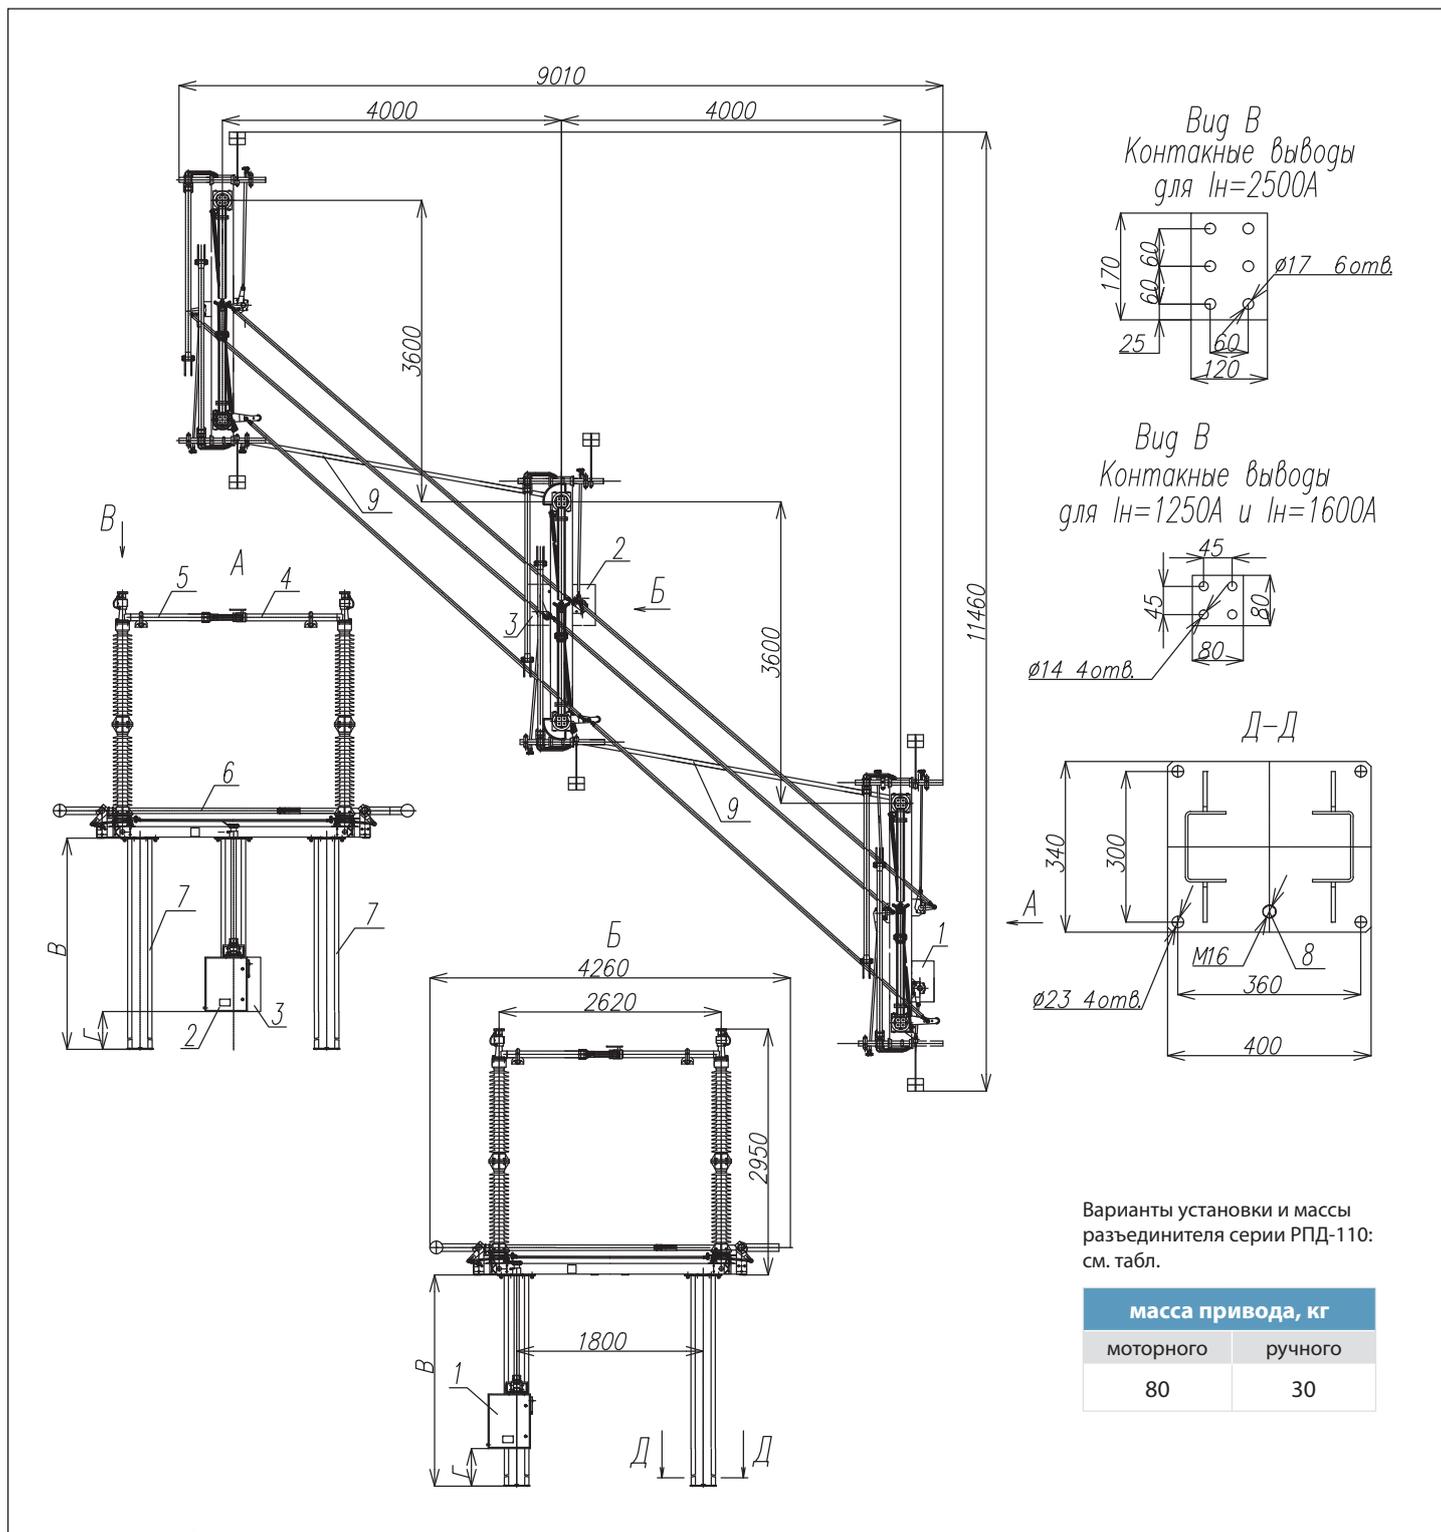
Разъединитель трехполюсный серии РПД-110 ступенчато-килевого исполнения
